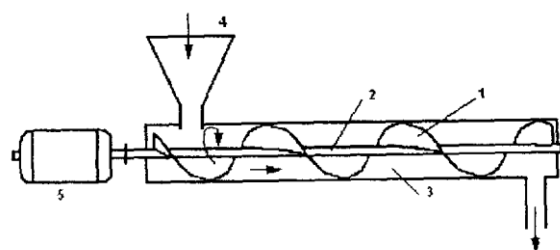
Схема шнекового транспортера: 1 - лопасти шнека (винт); 2 - вал шнека; 3 - полый цилиндр; 4 - загрузочный бункер; 5 -приводная станция
